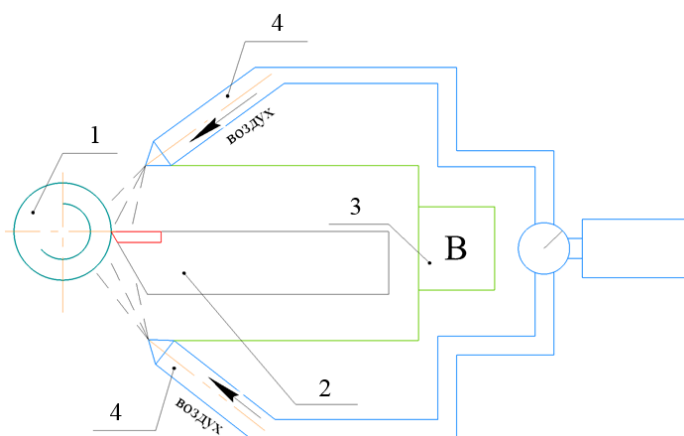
Подача ионизированного воздуха по двухсопловой схеме: 1 – заготовка; 2 – резец; 3 – установка «Варкаш»; 4 – сопловой аппарат с коронирующим электродом
